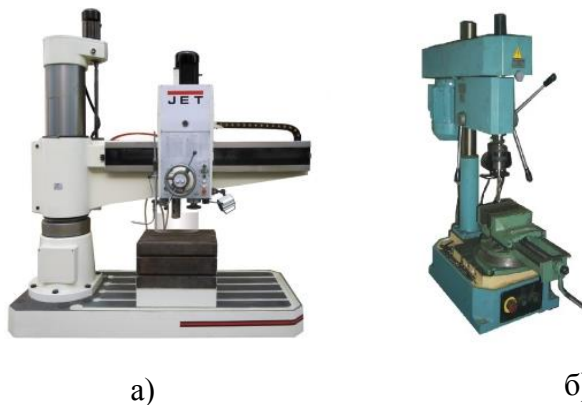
Типы сверлильных станков (а – радиально-сверлильный станок, б - вертикально-сверлильный станок)
